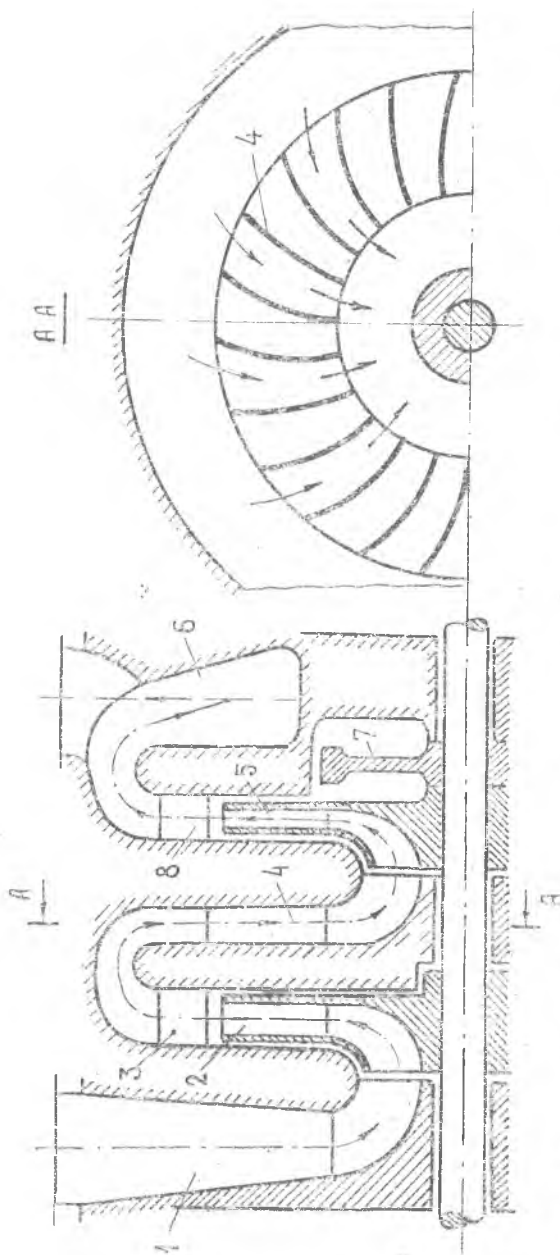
Схема двухступенчатой центробежной машины: 1 — входное устройство (подвод); 2 — рабочее колесо 1-й ступени; 3, 8 — диффузор; 4 — обратный направляющий аппарат; 5 — рабочее колесо 2-й ступени; 6 — улитка (отвод); 7 — разгрузочный диск
